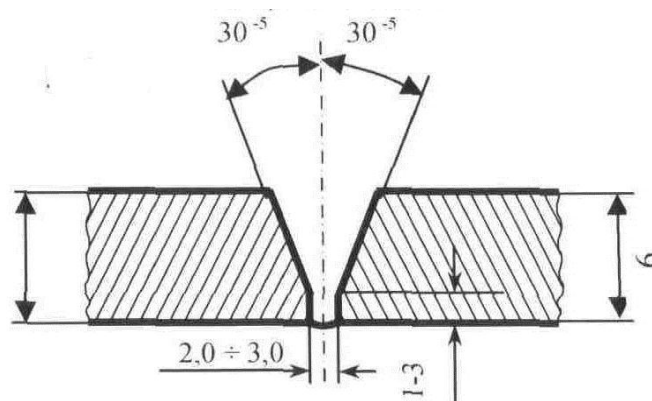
Технологическая схема сборки и ручной дуговой сварки пластин электродами.
